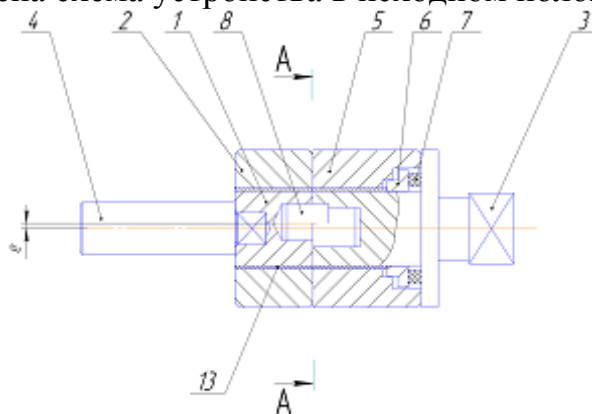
Схема устройства для резки труб одновременным сдвигом и кручением.
